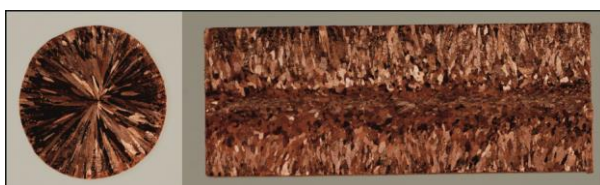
Makrostruktura przekroju poprzecznego i wzdłużnego pręta z miedzi w gatunku Cu-OFE uzyskanego w procesie ciągłego odlewania w warunkach przemysłowych na instalacji Upcast przy prędkości odlewania 2,0 m/min. oraz przy przepływie wody chłodzącej krystalizator 50 l/min.
